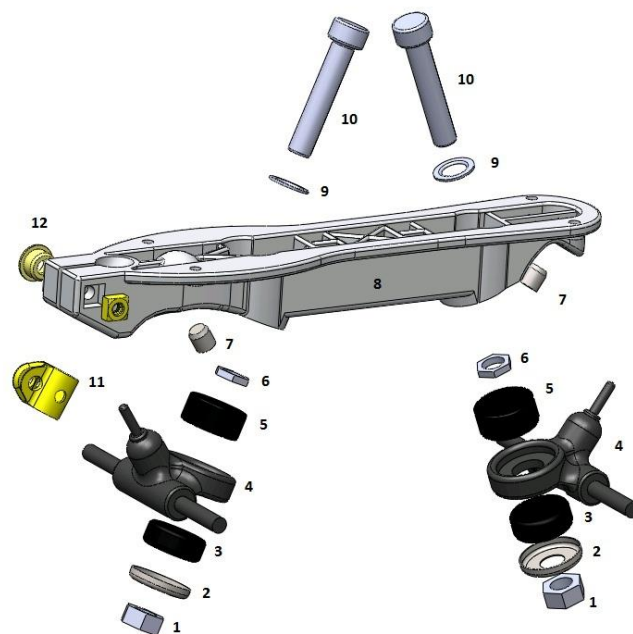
Vista explodida dos componentes do patim com base polimérica
